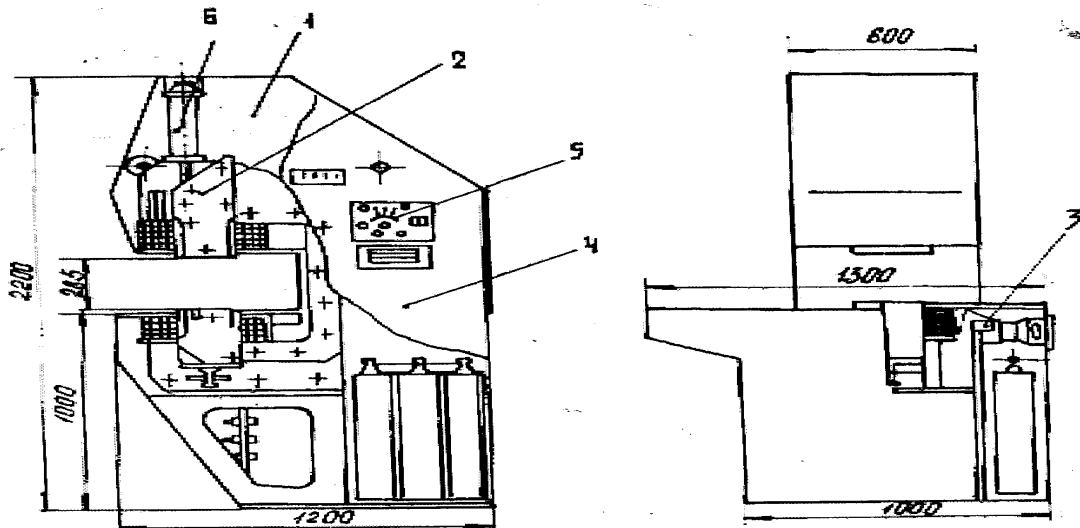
Индукционная установка ТПЧ для нагрева под сборку деталей локомотива: 1 - корпус, 2 - индуктор, 3 - механизм ввода термопары, 4 - шкаф с электроаппаратурой, 5 - панель управления, 6 - пневмопривод.
